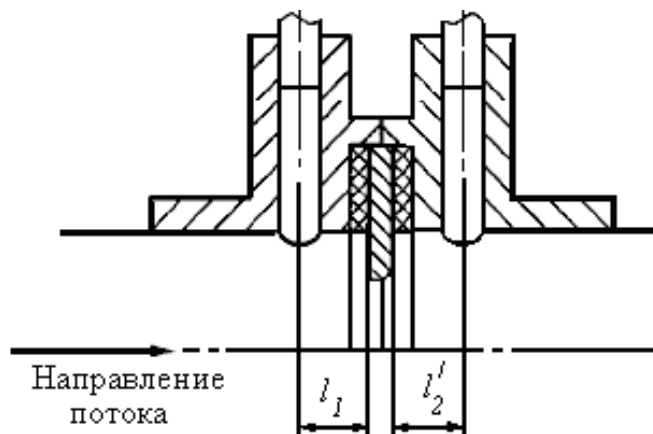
Расположение отверстий для фланцевого способа отбора давления
